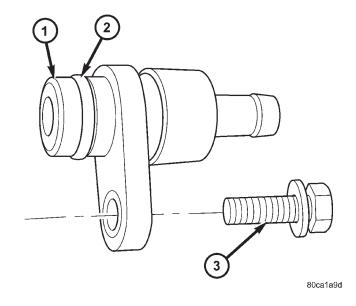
VALVULA DE PCV Y ANILLO O - 2.4L
